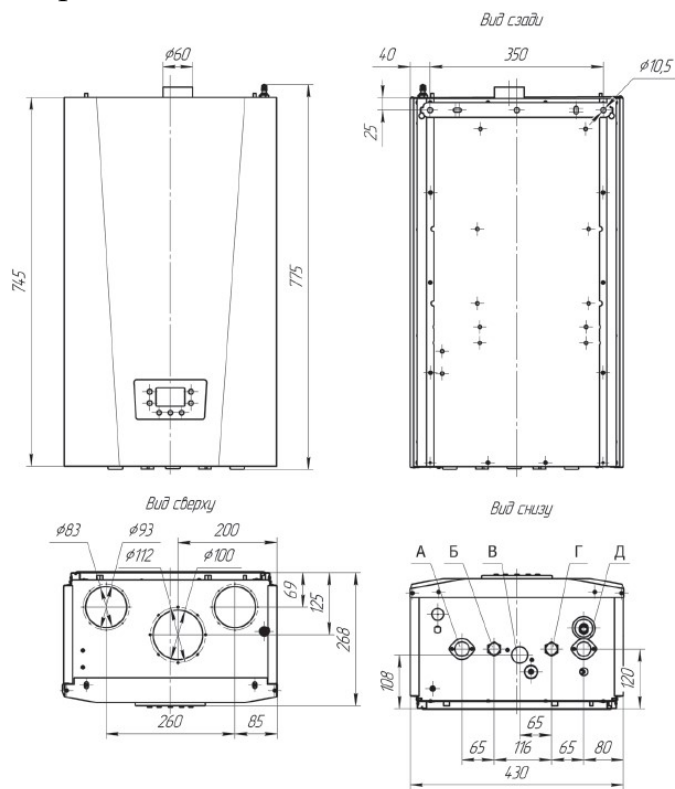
Габаритные размеры газового двухконтурного котла «Ле-макс» Prime-V24
